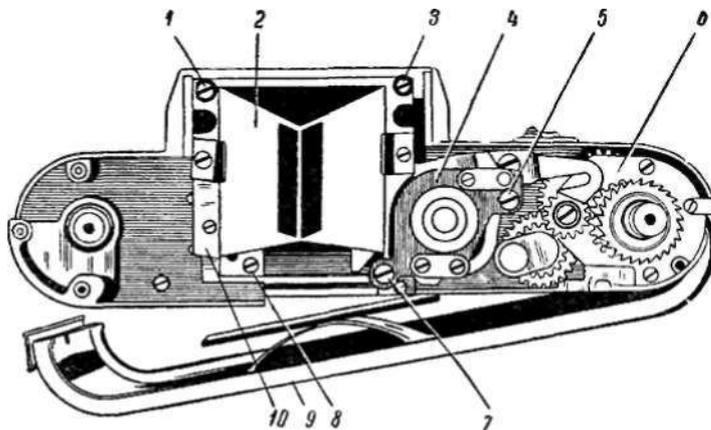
Механизмы фотоаппарата «Кристалл»: 1, 3, 5, 7 и 8— винты; 2— пентапризма; 4— плата синхро устройства; 6— узел шестерен заводного механизма; 9— откидная крышка; 10— основание пентапризмы
